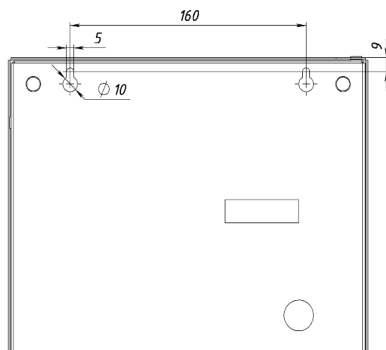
Установочный чертёж прибора (вид сзади)
